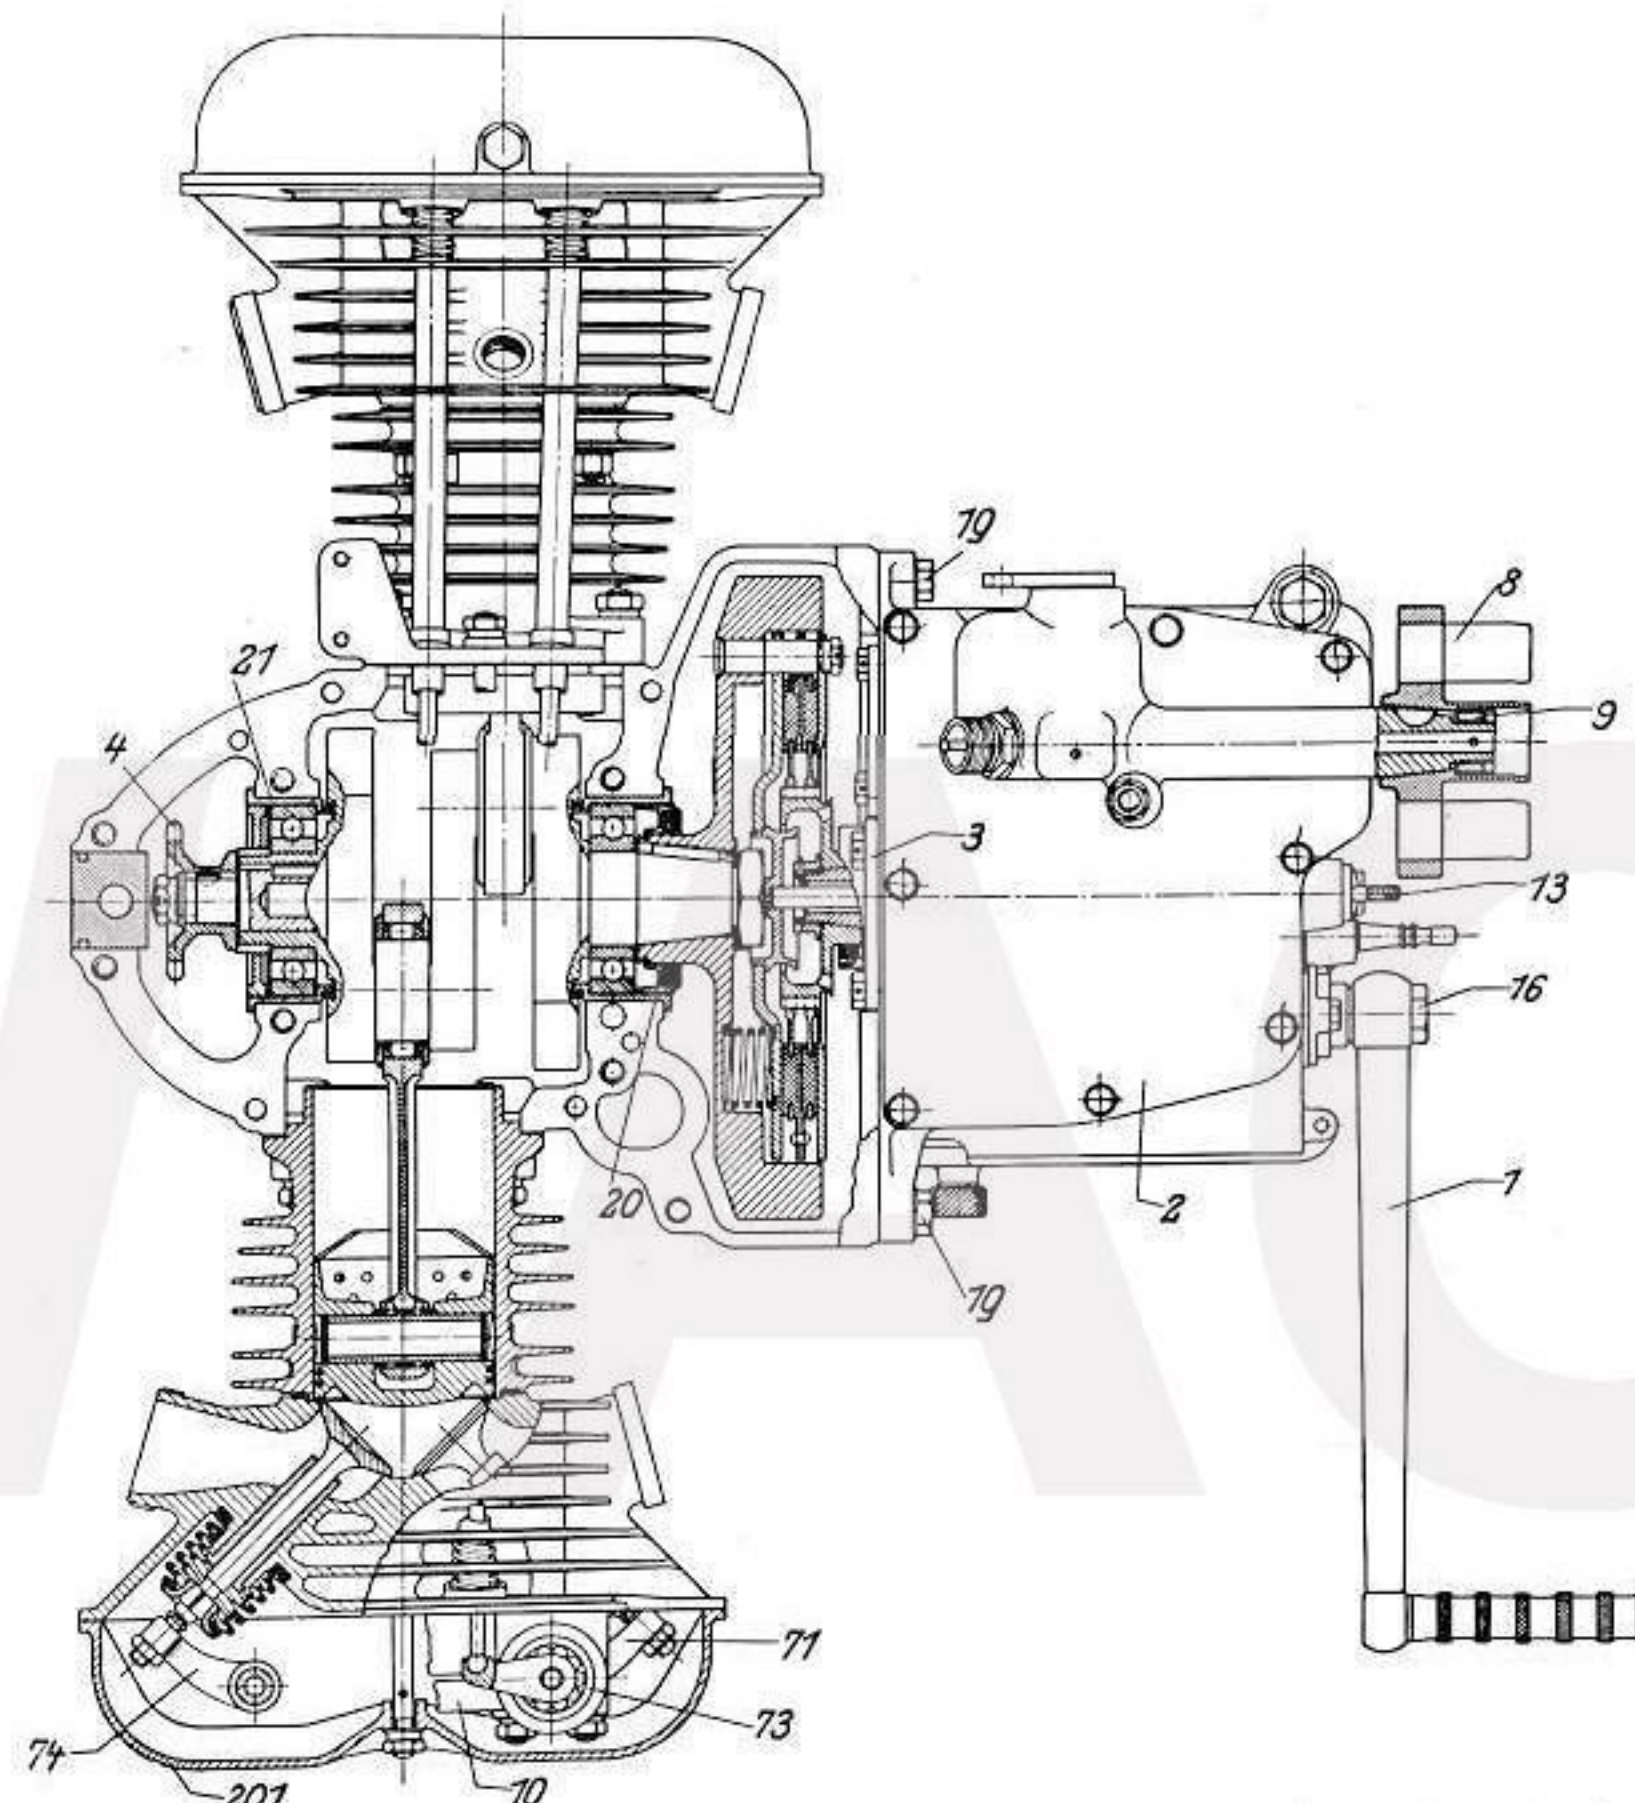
Sportmotor mit teilweisem Horizontalschnitt durch die Zylindermitte
